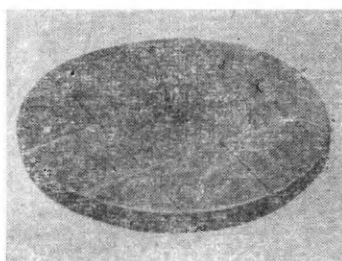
Металлический (чугунный) шлифовальник, подготовленный к обработке зеркала с отверстием в центре.
